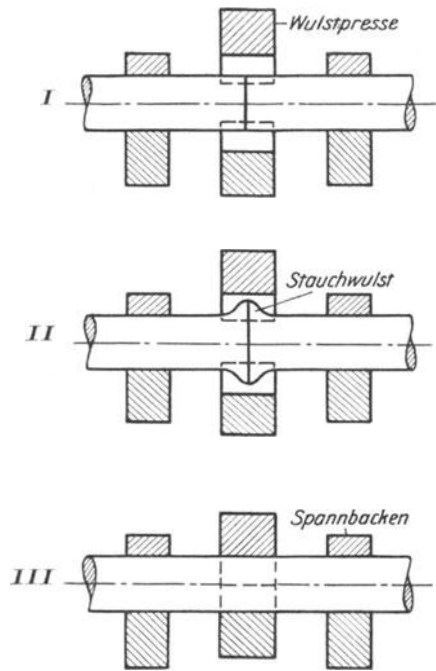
Schema der Wulstpressung bei Kettengliedern.
